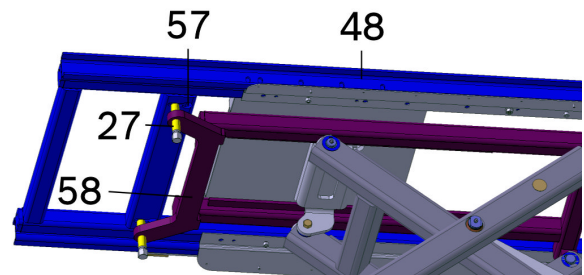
Ножничный подъемный стол без платформ, вид снизу
